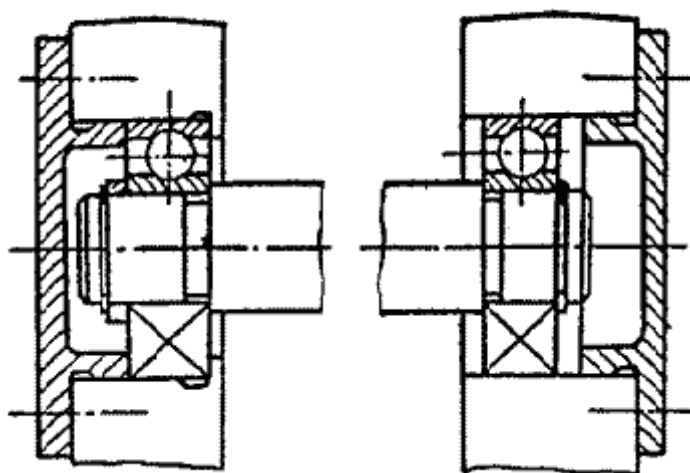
Установка вала с одной плавающей и одной фиксирующей опорой.
